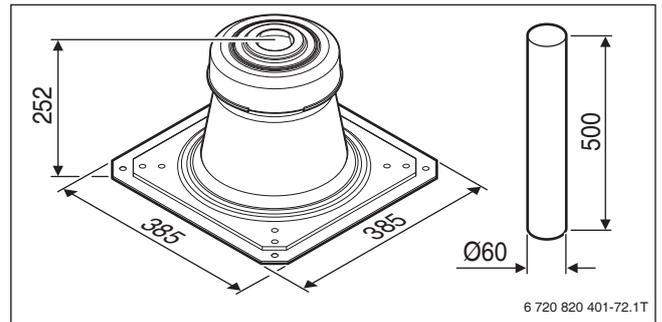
Schachtabdeckung für 60 mm, Kunststoff (Maße in mm)
